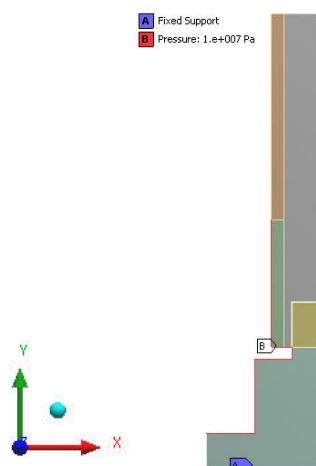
Сечение корпуса гидроцилиндра с внешними нагрузками
